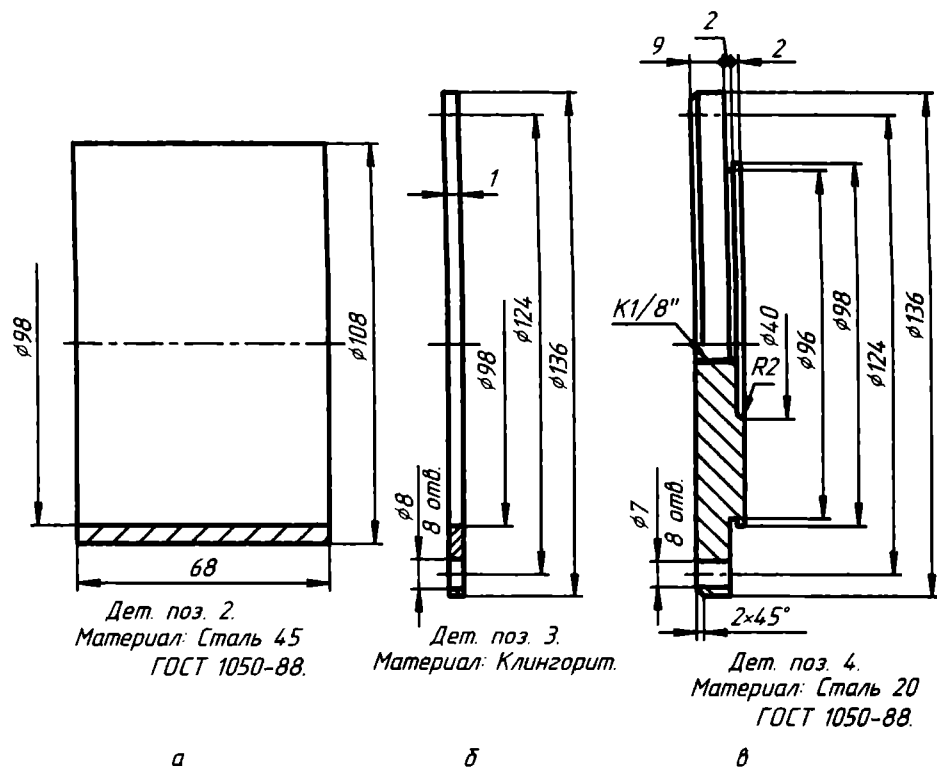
Чертежи: а — гильзы; б — прокладки; в — крышки
